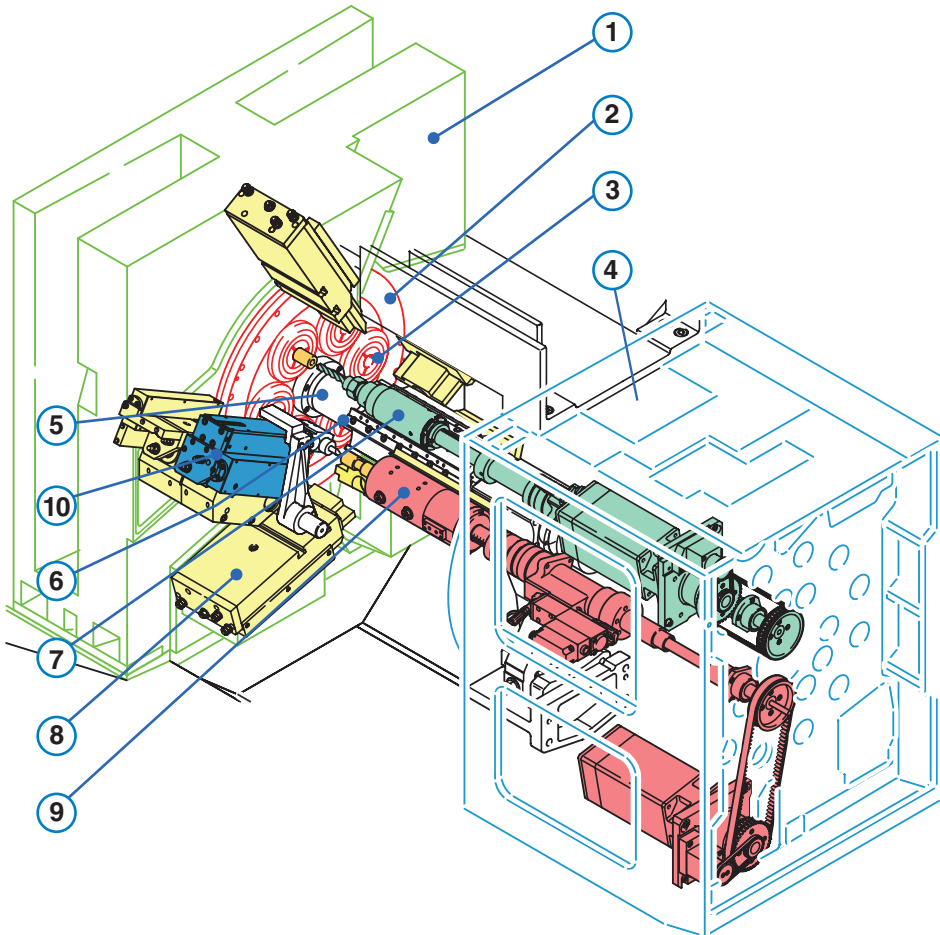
Aufbau eines CNC-Mehrspindel-Drehautomaten mit hydraulischer Antriebstechnik. [Bildquelle: Schütte]
